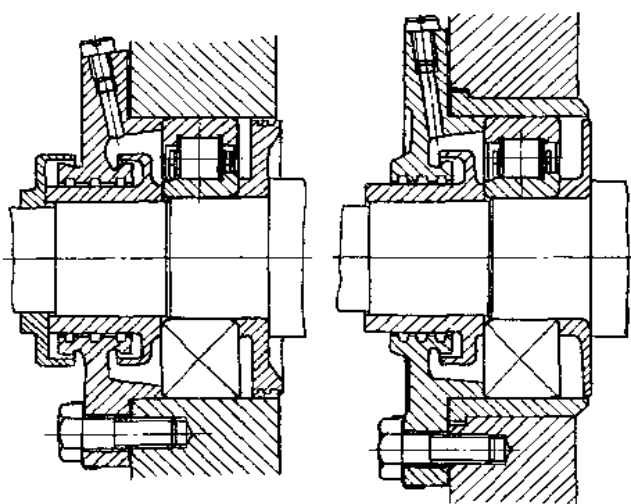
用润滑脂时减速箱轴承的内部结构
